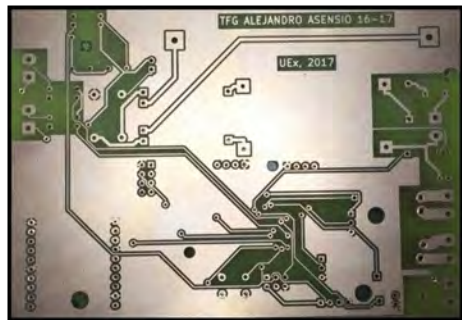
Imagen del PCB por lado de las soldaduras.
